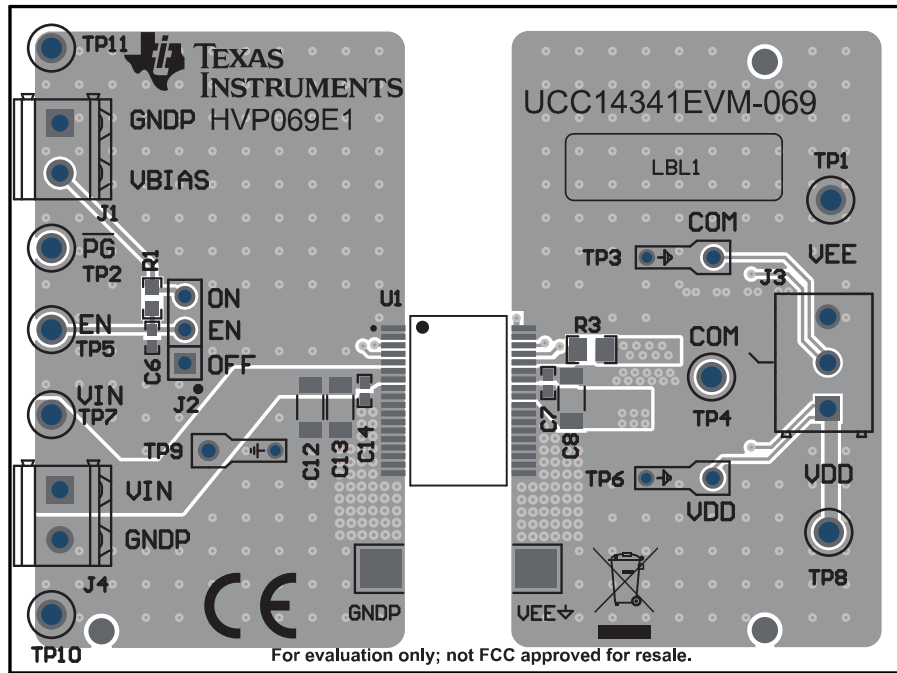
UCC14341EVM-069 , PCB 顶层, 组装
